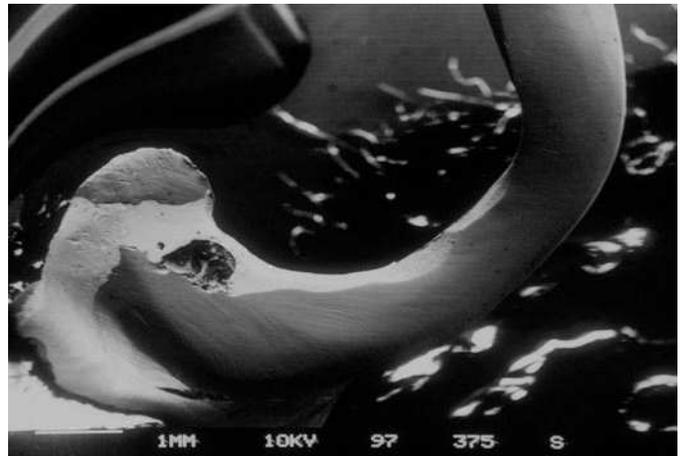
Una soldadura indirecta claramente visible en la zona del gancho (13).
